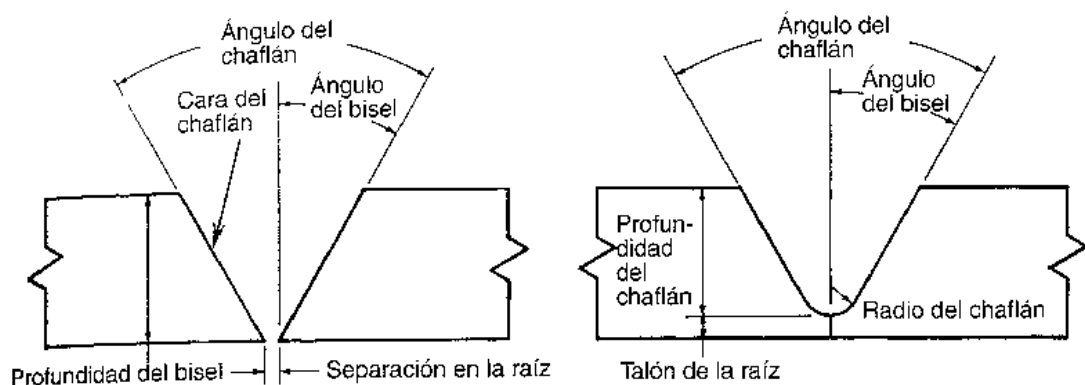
Preparación del borde de chapa para soldaduras
